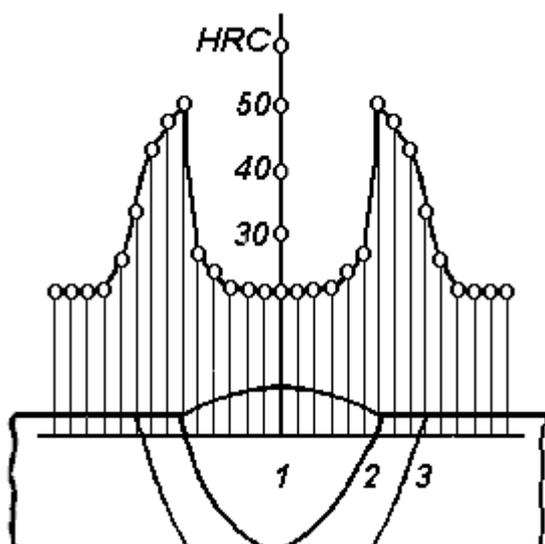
Распределение твёрдости по сечению сварного соединения из закаливающейся стали
